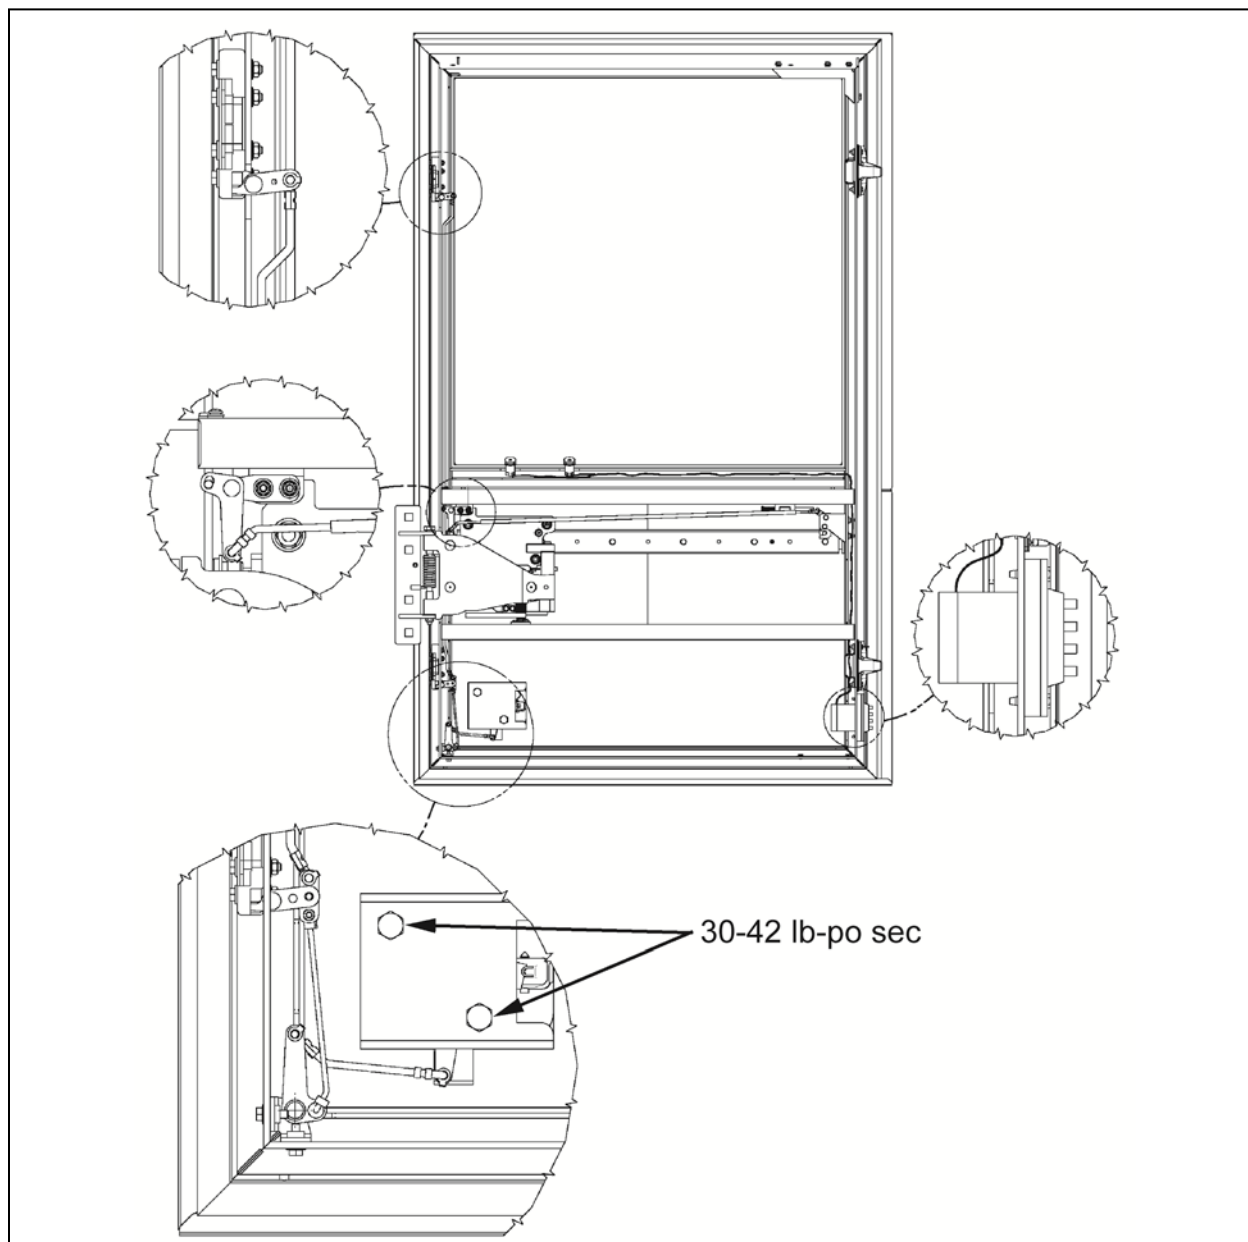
MÉCANISME D'OUVERTURE DE LA PORTE COULISSANTE D'ACCÈS À L'ÉLEVATEUR POUR FAUTEUILS ROULANTS
